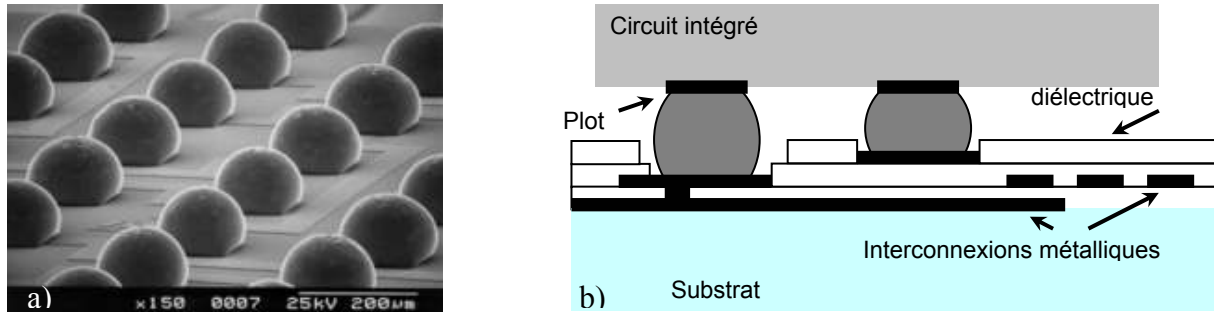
Photographie de boules de soudure en vue d'un report Flip Chip. Principe d'un report Flip Chip
